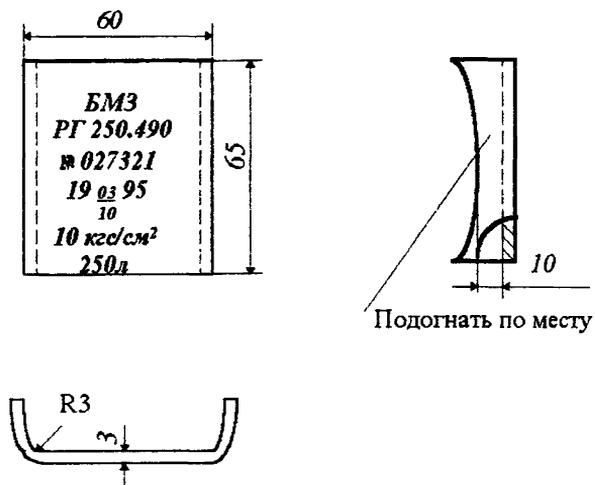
Образец таблички с указанием паспортных данных резервуара
